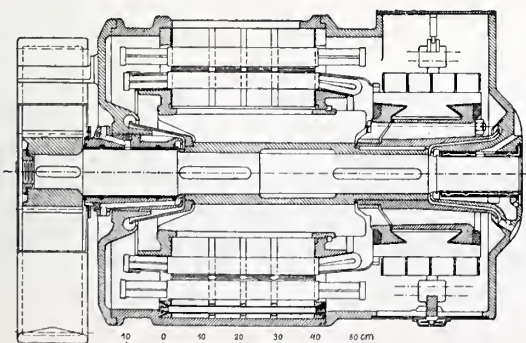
Einphasenwechselstrom-Vorgelegemotor der Siemens-Schuckertwerke für Seebach-Wettingen. — 1:20.
